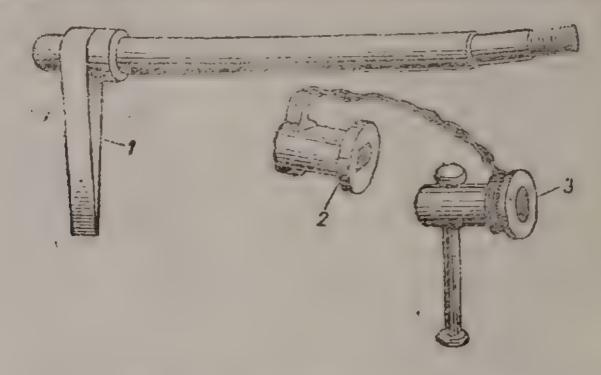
Соединительный болт: 1—голопка с хностом; 2— шайба; 3— гайка с воротком
